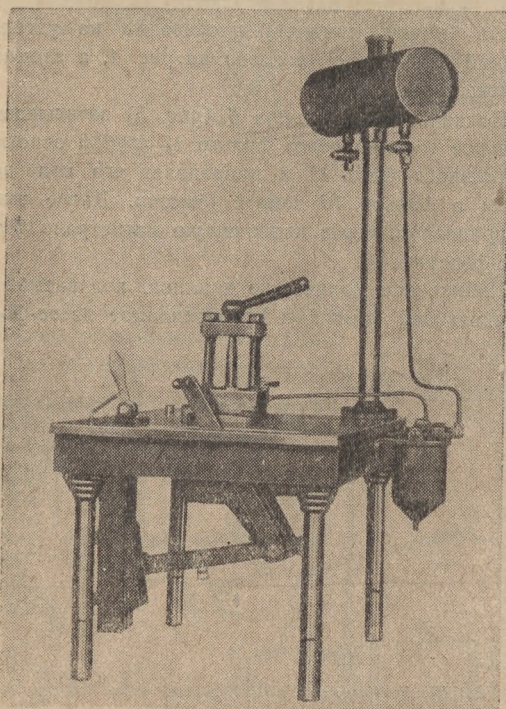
Общий вид установки для испытания плунжерной пары на герметичность.
